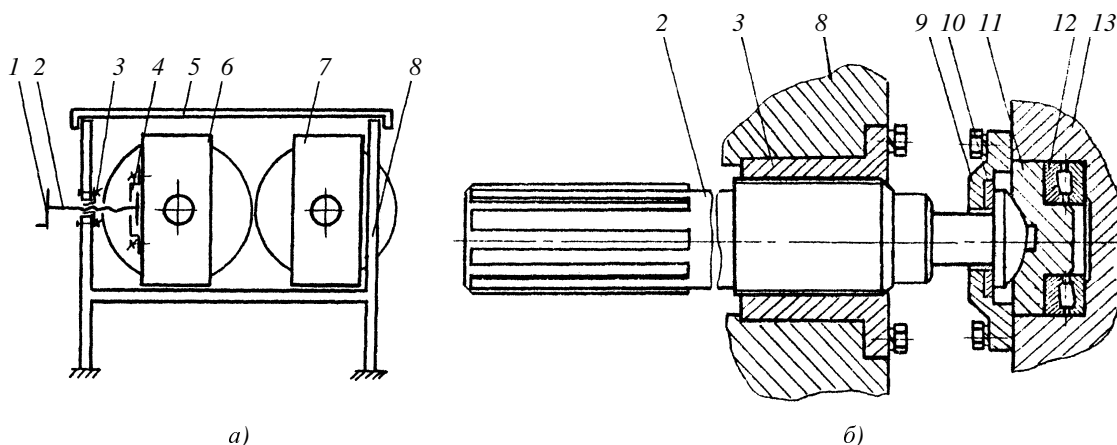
Кінематична схема механізму регулювання зазору вальців (а) і схема вузла гвинта упорного (б): 1 – привід гвинта упорного; 2 – гвинт упорний; 3 – гайка; 4 – упорний підшипник; 5 – траверса; 6 – рухомий підшипник переднього валка; 7 – нерухомий підшипник заднього валка; 8 – станина; 9 – кришка; 10 – шайба; 11 – п'ята; 12 – упорний ролик-підшипник; 13 – корпус валкового підшипника
